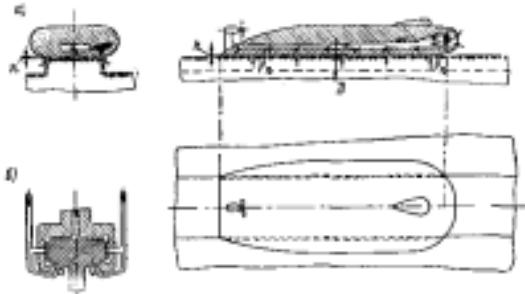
Схема машины четвертого типа: а — юз под воздушной смазкой; б — юз под воздушной смазкой в ролике.
